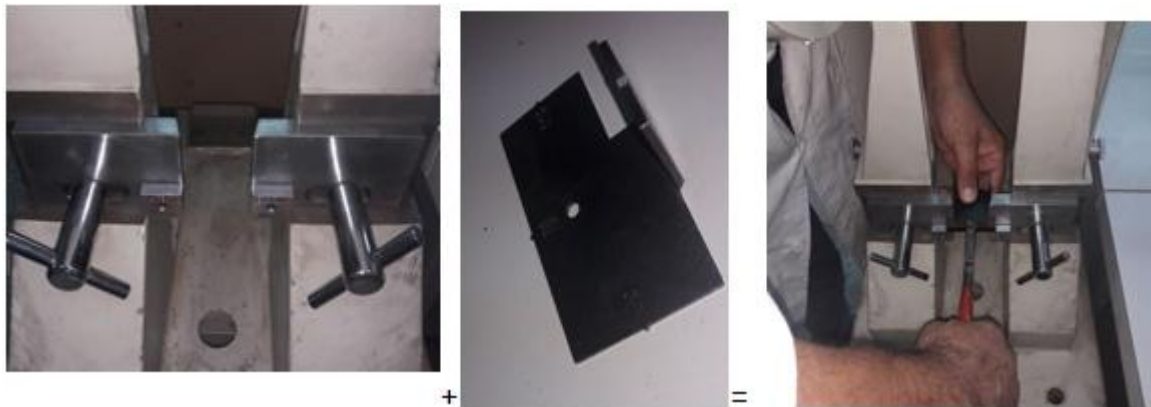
Le calibrage de l'éprouvette sur le porte échantillon pour que l'impact
